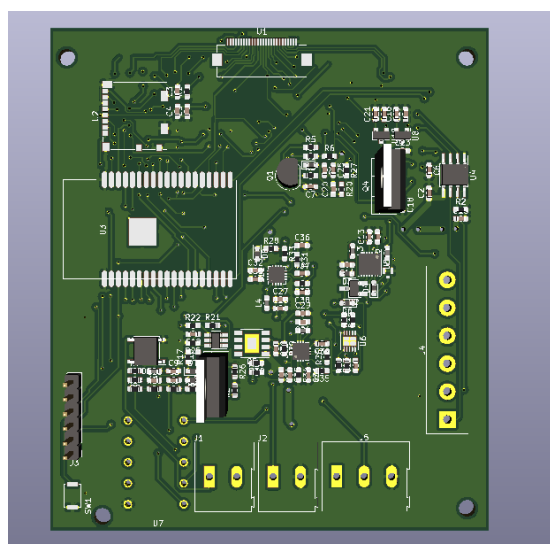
PCB Vista Frontal (Elaboración Propia)
